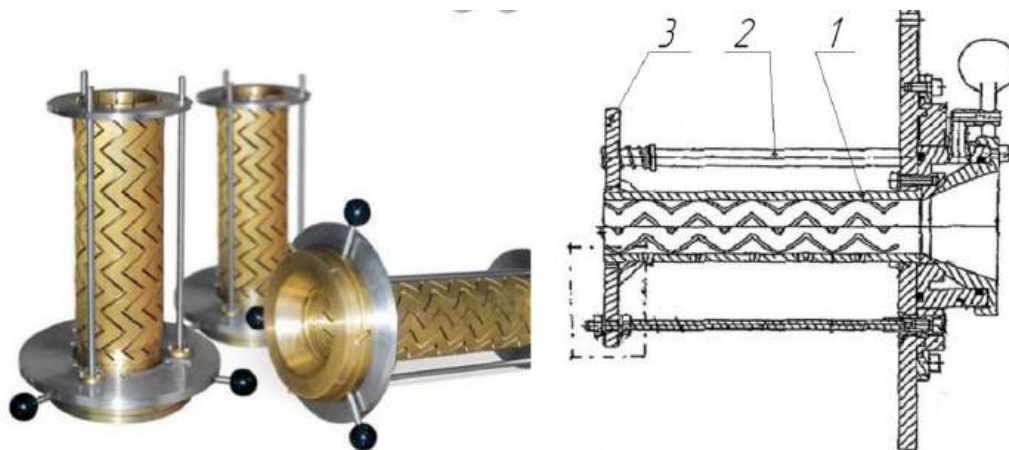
Калібрувальний пристрій з конічною формою калібрувальної гільзи [48]
